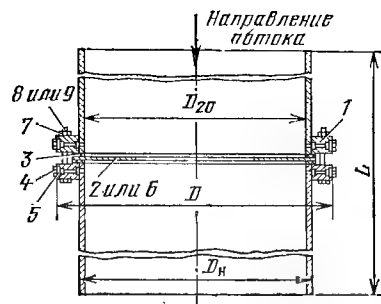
Установка монтажного кольца или дисковой диафрагмы. 1 — фланец с патрубком; 2 — кольцо монтажное; 3 — прокладка; 4 — пробка; 5 — прокладка; 6 — диафрагма ГОСТ 14322-77; 7 — гайка; 8 — болт; 9 — шпилька.
